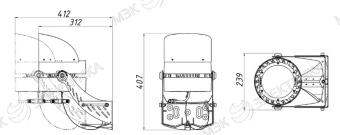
Общий вид светильника L-industry II с регулируемым поворотным креплением.
